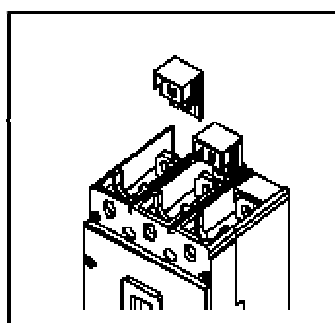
Подготовка присоединения с винтовыми зажимами с автоматами SENTRON VL250, VL400 und VL630.
